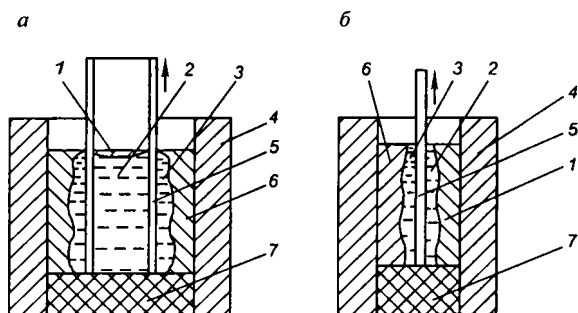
Схемы получения биметаллических заготовок в кокилях:
